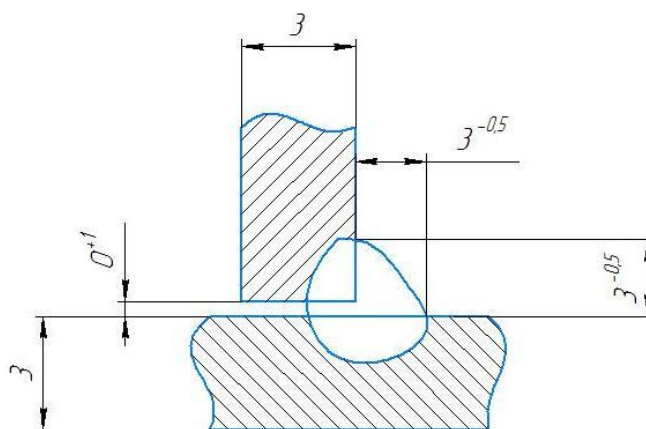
Геометрические размеры площади наплавленного металла без разделки кромок
